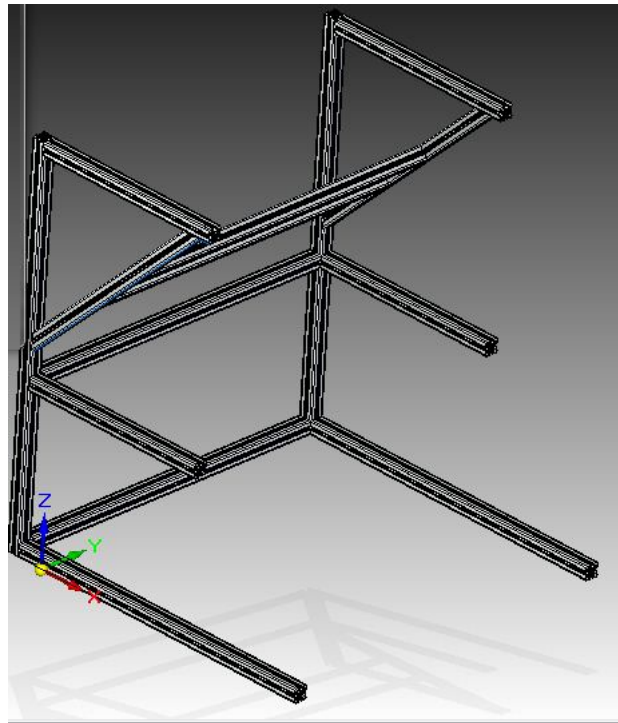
Ensamble final de diseño del prototipo de inmersión
